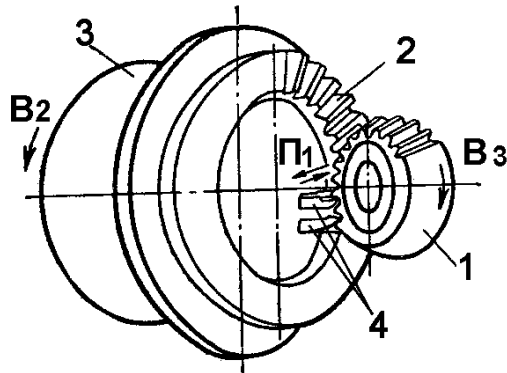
Схема относительного положения заготовки и производящего колеса: 1 – заготовка; 2 – воображаемое плосковершинное колесо; 3 – люлька; 4 – резцы, режущие кромки которых расположены там, где должны находиться боковые стороны одного из зубьев производящего колеса
